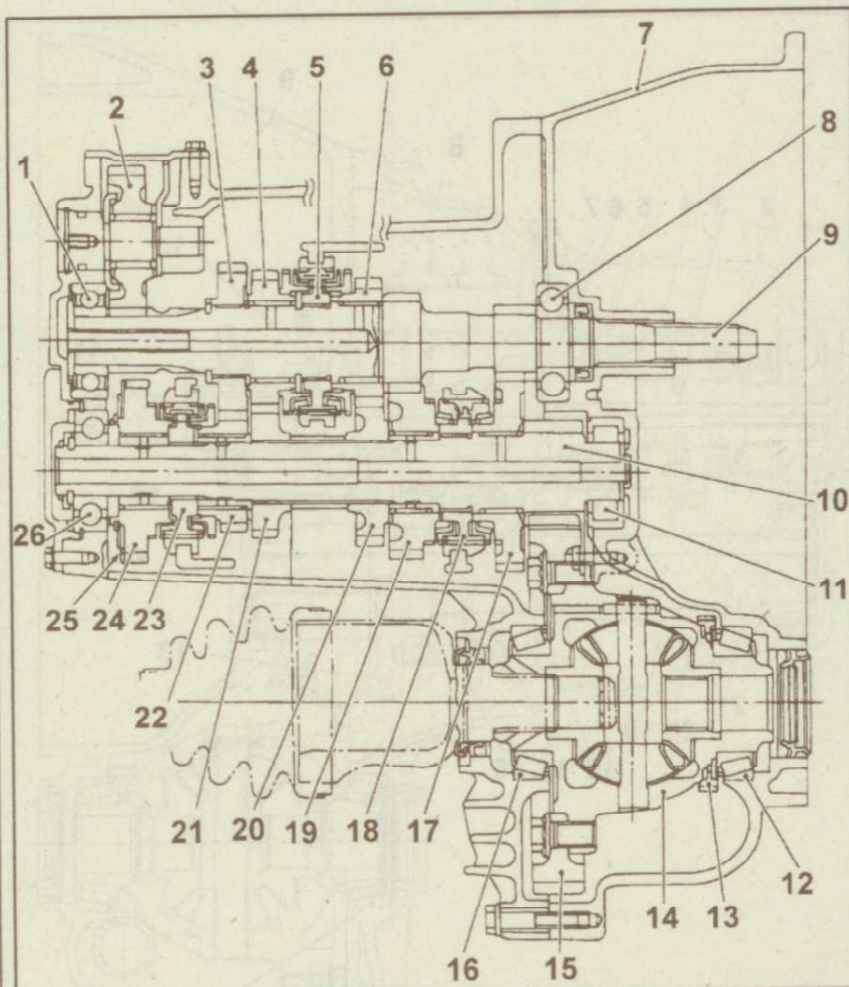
Разрез коробки передач RS5F70A: 1 – задний подшипник первичного вала; 2 – промежуточная шестерня передачи заднего хода; 3 – шестерня 5-й передачи первичного вала; 4 – шестерня 4-й передачи первичного вала; 5 – синхронизатор 3-й/4-й передач; 6 – шестерня 3-й передачи первичного вала; 7 – картер сцепления; 8 – передний подшипник первичного вала; 9 – первичный вал; 10 – вторичный вал; 11 – передний подшипник вторичного вала; 12 – подшипник дифференциала; 13 – шестерня привода спидометра; 14 – коробка дифференциала; 15 – главная передача; 16 – подшипник дифференциала; 17 – шестерня 1-й передачи вторичного вала; 18 – синхронизатор 1-й/2-й передач с двойным блокирующим кольцом; 19 – шестерня 2-й передачи вторичного вала; 20 – шестерня 3-й передачи вторичного вала; 21 – шестерня 4-й передачи вторичного вала; 22 – шестерня 5-й передачи вторичного вала; 23 – синхронизатор 5-й передачи и передачи заднего хода; 24 – шестерня передачи заднего хода вторичного вала; 25 – промежуточная шестерня; 26 – задний подшипник вторичного вала
